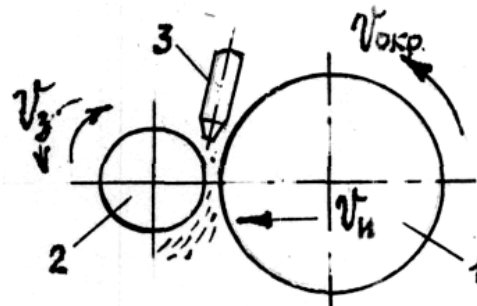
Схема електроерозійного шліфування: 1 – електрод-інструмент; 2 – заготовка; 3 – насад
